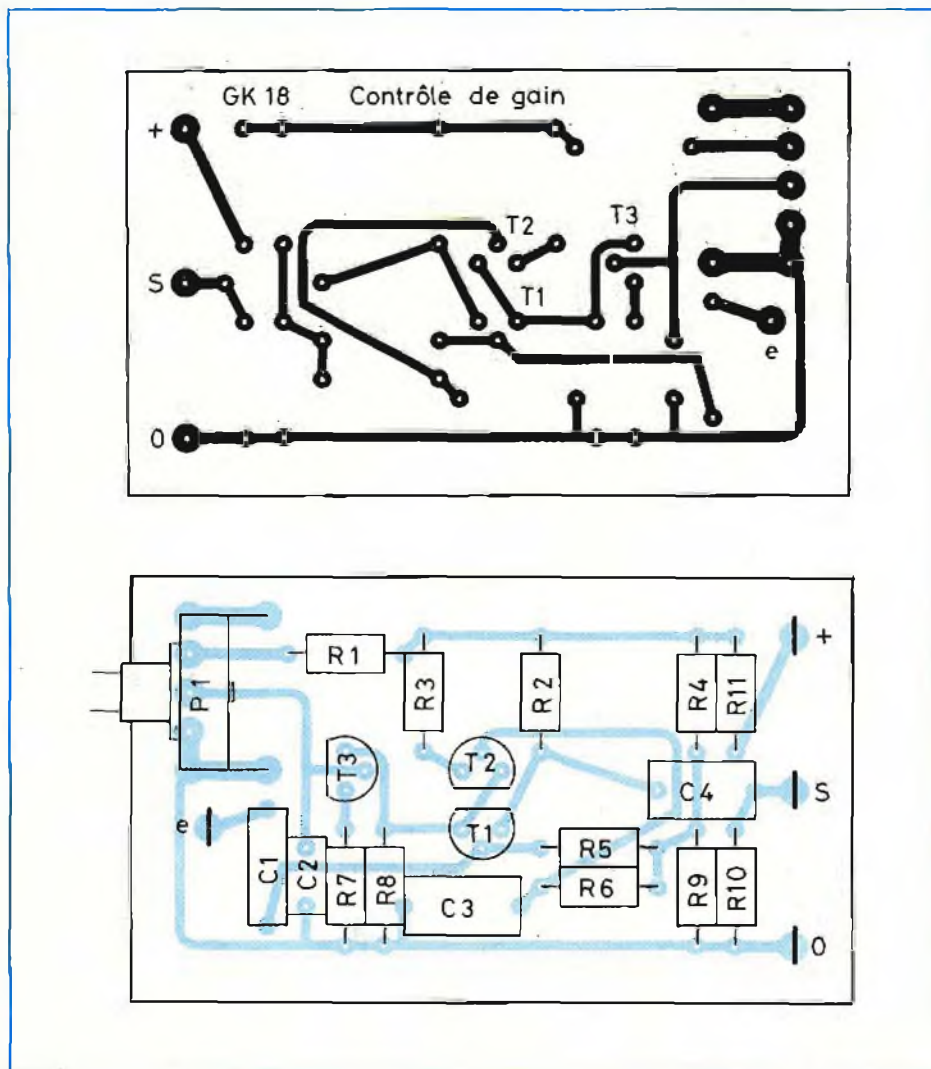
In alto (A) lato rame del circuito stampato su cui può essere montato il dispositivo di controllo automatico del guadagno, ed in basso (B) il lato dei componenti.
